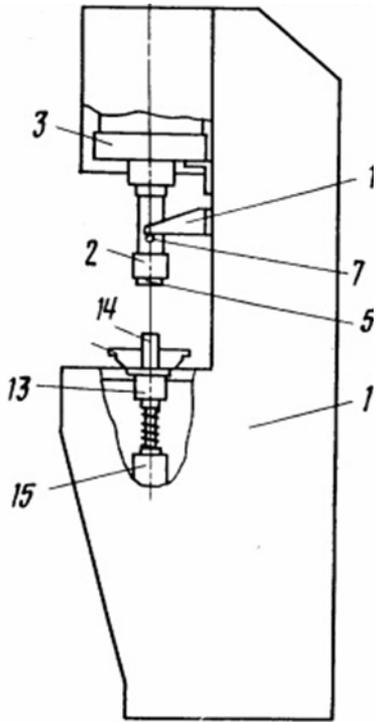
Устройство для запрессовки манжет и подшипников в корпус, общий вид (А.С. SU1344567)
